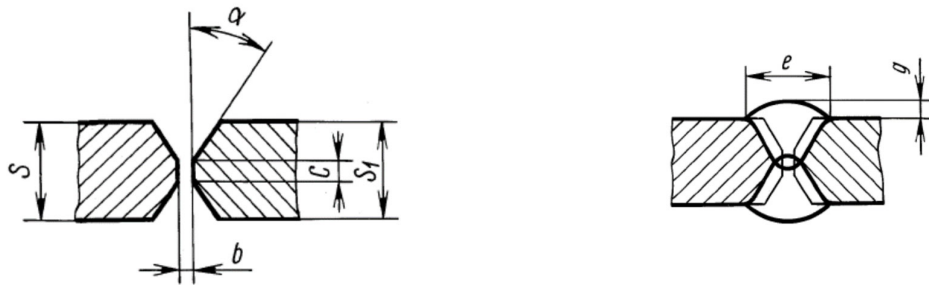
Вид з'єднання і конструктивні розміри зварного стикового шва (ГОСТ 14771-76, С25)
